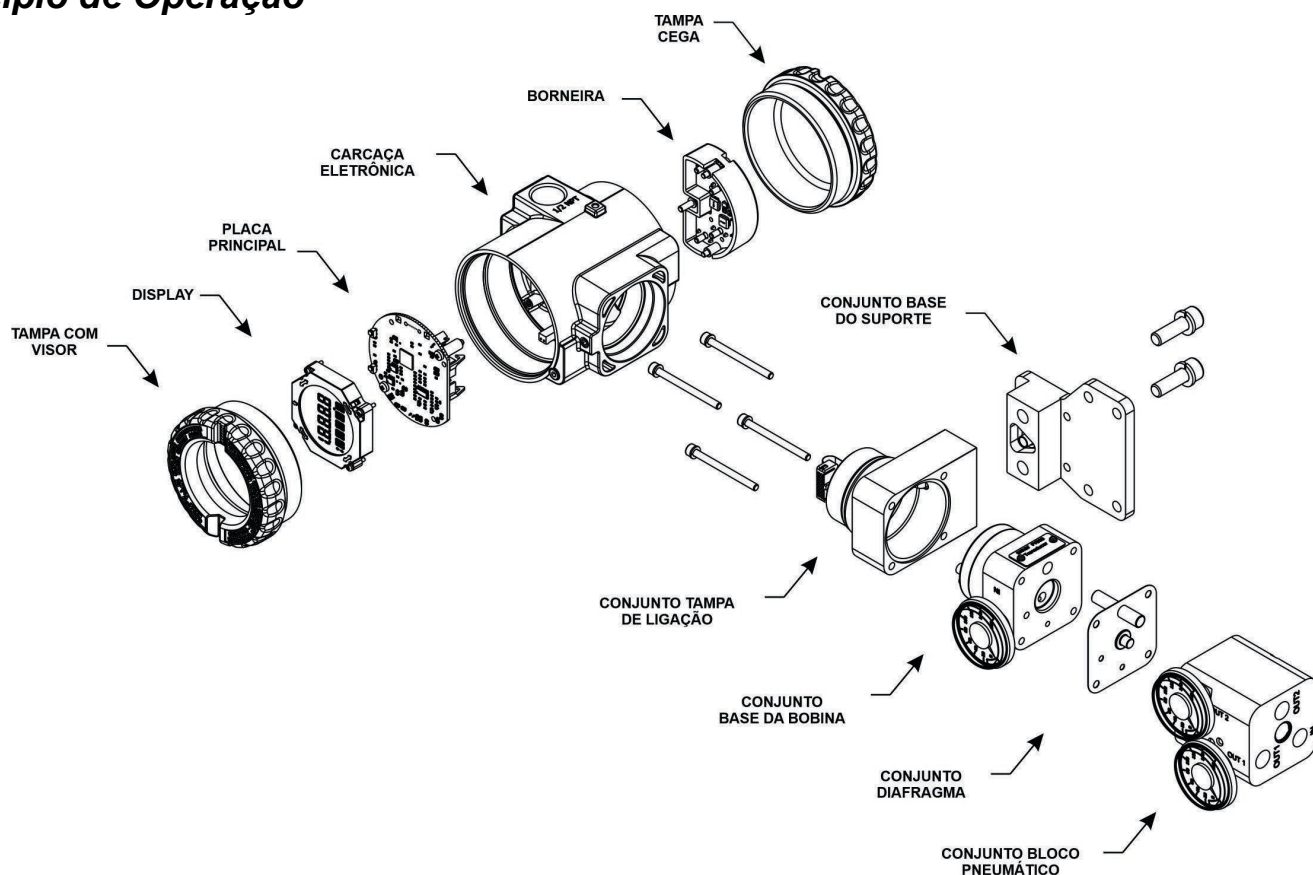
FY500 Posicionador Digital de Válvulas (Vista Explodida)
